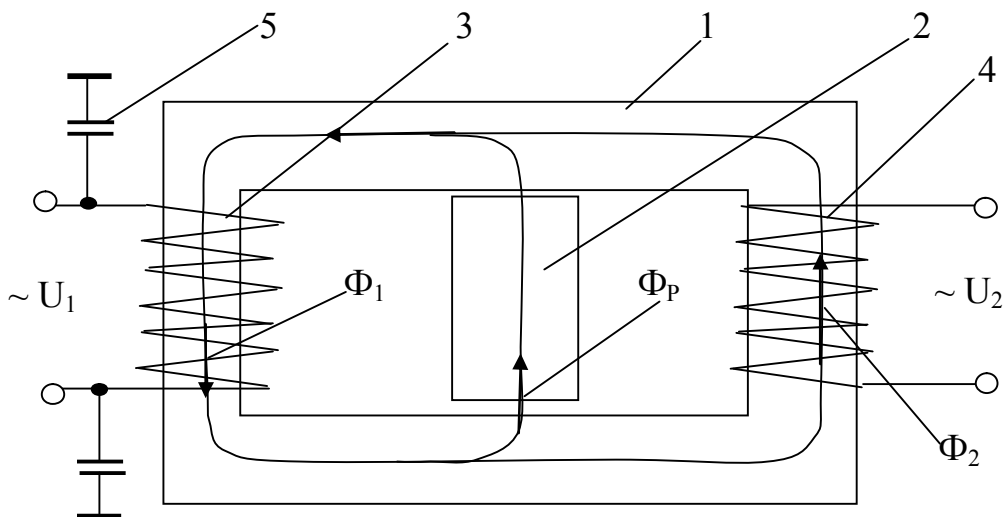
Принципиальная электромагнитная схема сварочного трансформатора СТШ-500:
